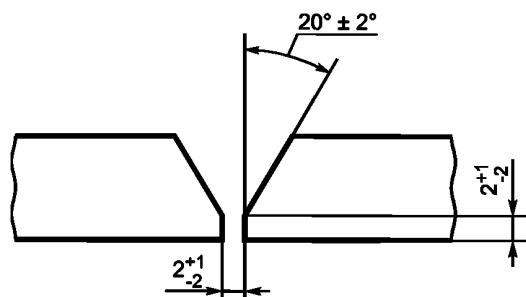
Конструктивные элементы подготовки кромок под сварку
